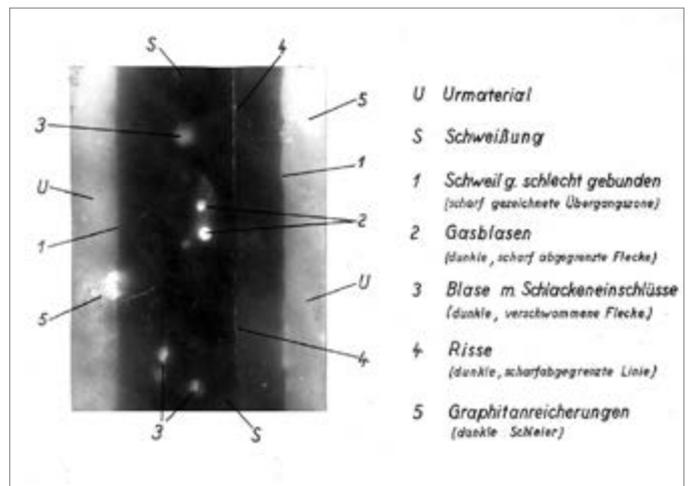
Erklärung typischer Schweißnahtfehler auf einem Röntgenfilm (1930)
